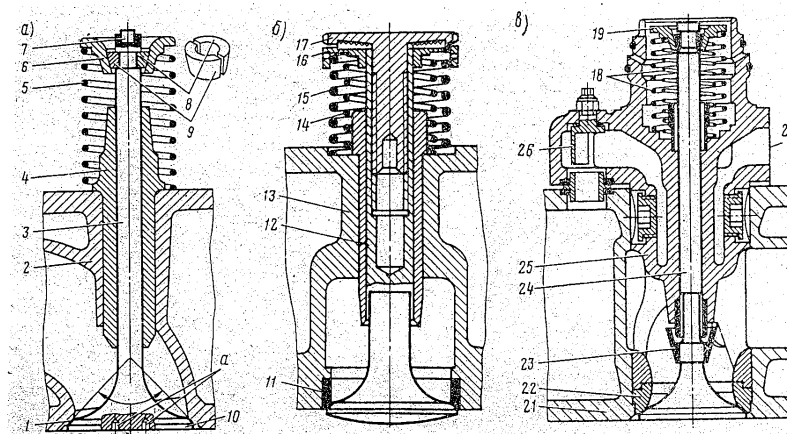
Типы клапанов рабочих цилиндров с нижним (а, в) и верхним (б) расположением распределительного вала
